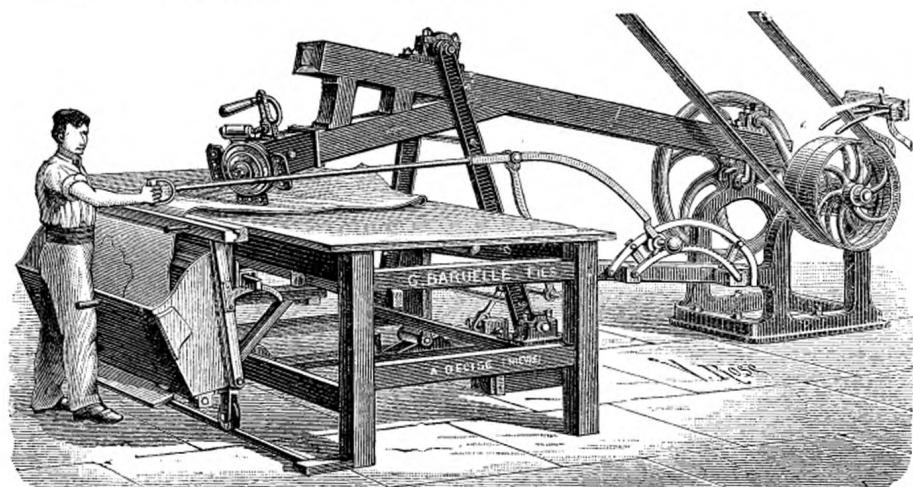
Machine à travailler les cuirs en corroirie de M. G. Baruelle.
